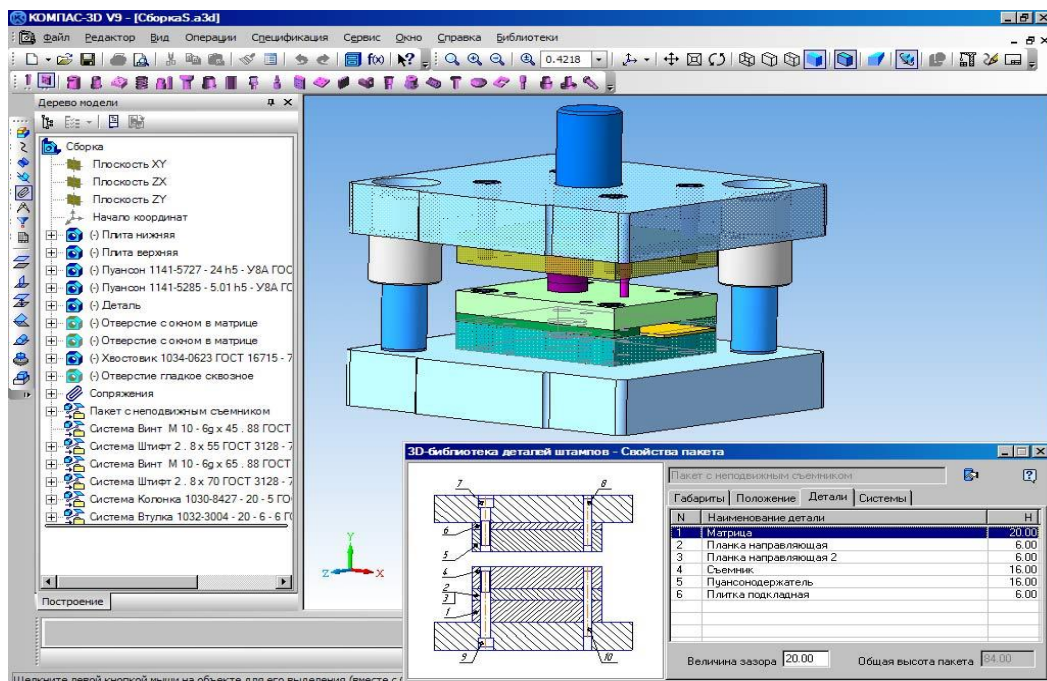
Пример 3d – сборки изделий в Компас–3d
